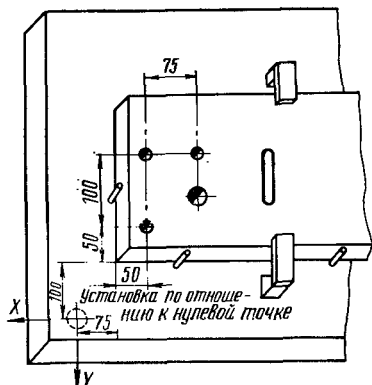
Базирование заготовки относительно нулевой точки станка
